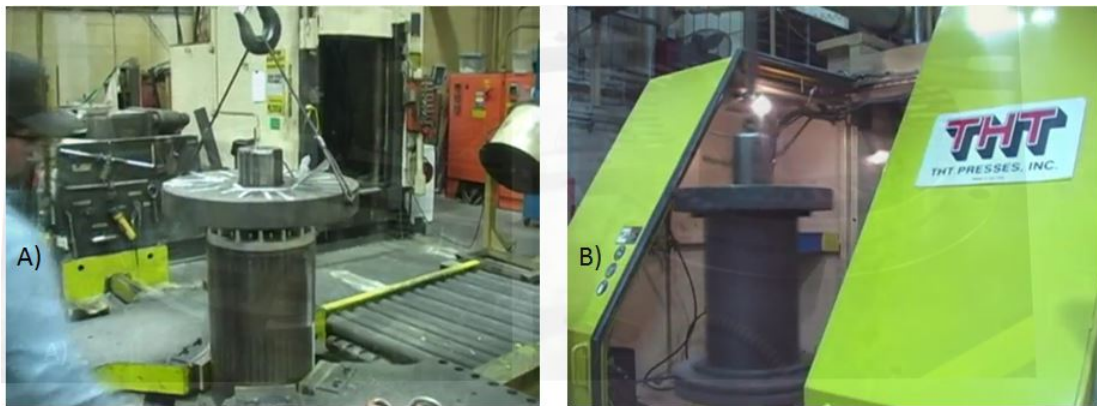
A) Rotor comprimido B) Rotor laminado a fundidor de precisión.
